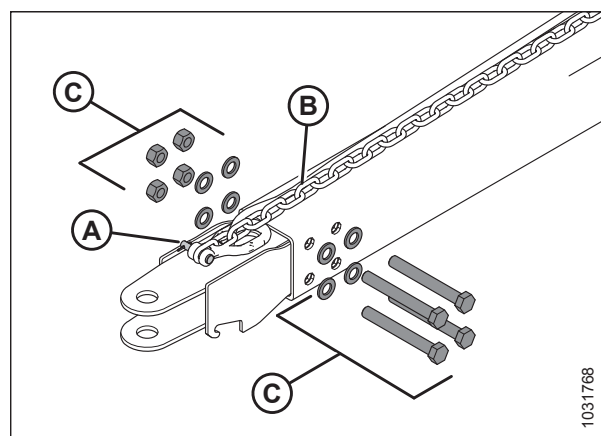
Demontarea adaptorului de remorcare pentru toartă
